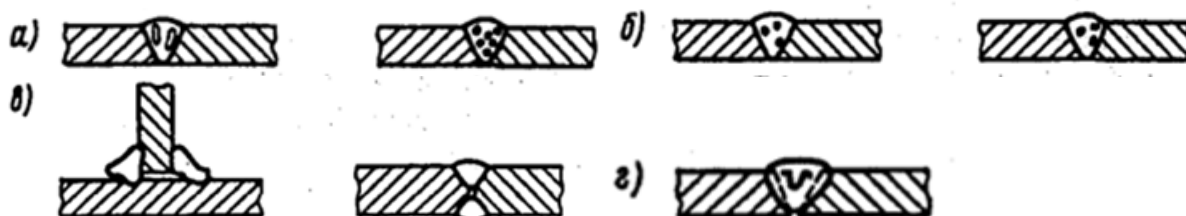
Внутренние дефекты сварного шва: а - поры (газовые включения); б - шлаковые и металлические включения; в - непровары; г – свищ
